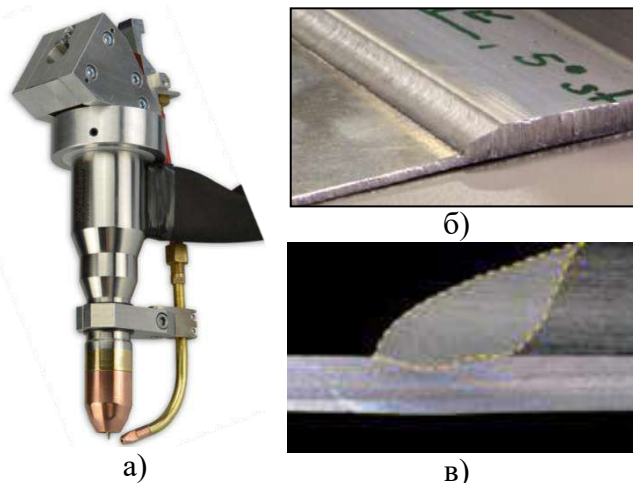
Оборудование для плазменной сварки: а) сварочная головка Kjellberg; б) послойная сварка изделия; в) сечение сварочного шва (информация с сайта www.kjellberg.de)
